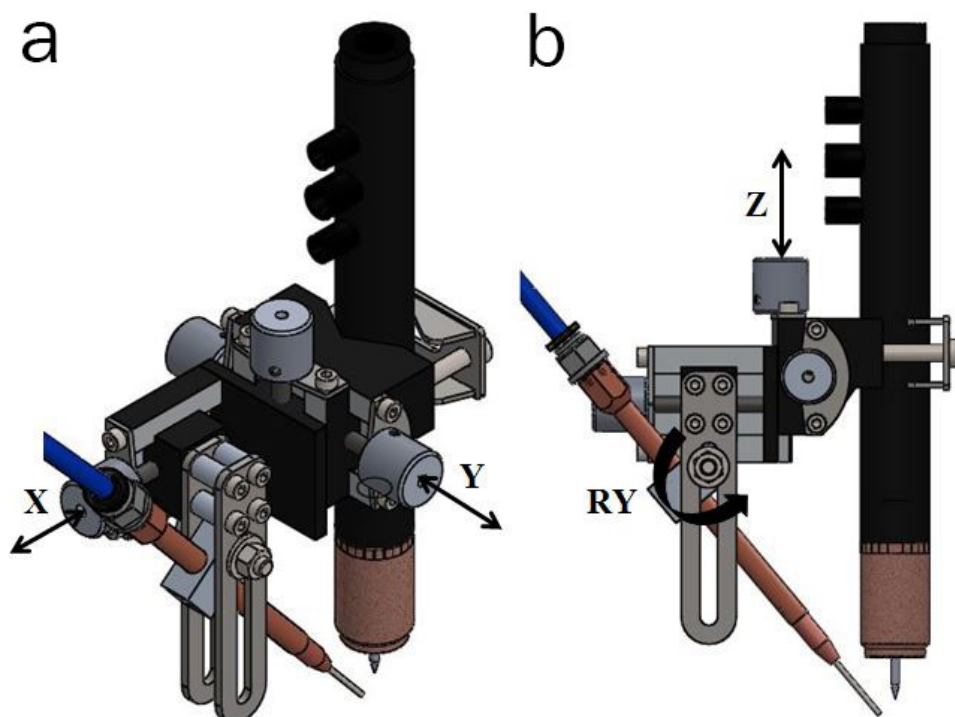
Dispositivo projetado. a) Vista isométrica. b) Vista lateral.
